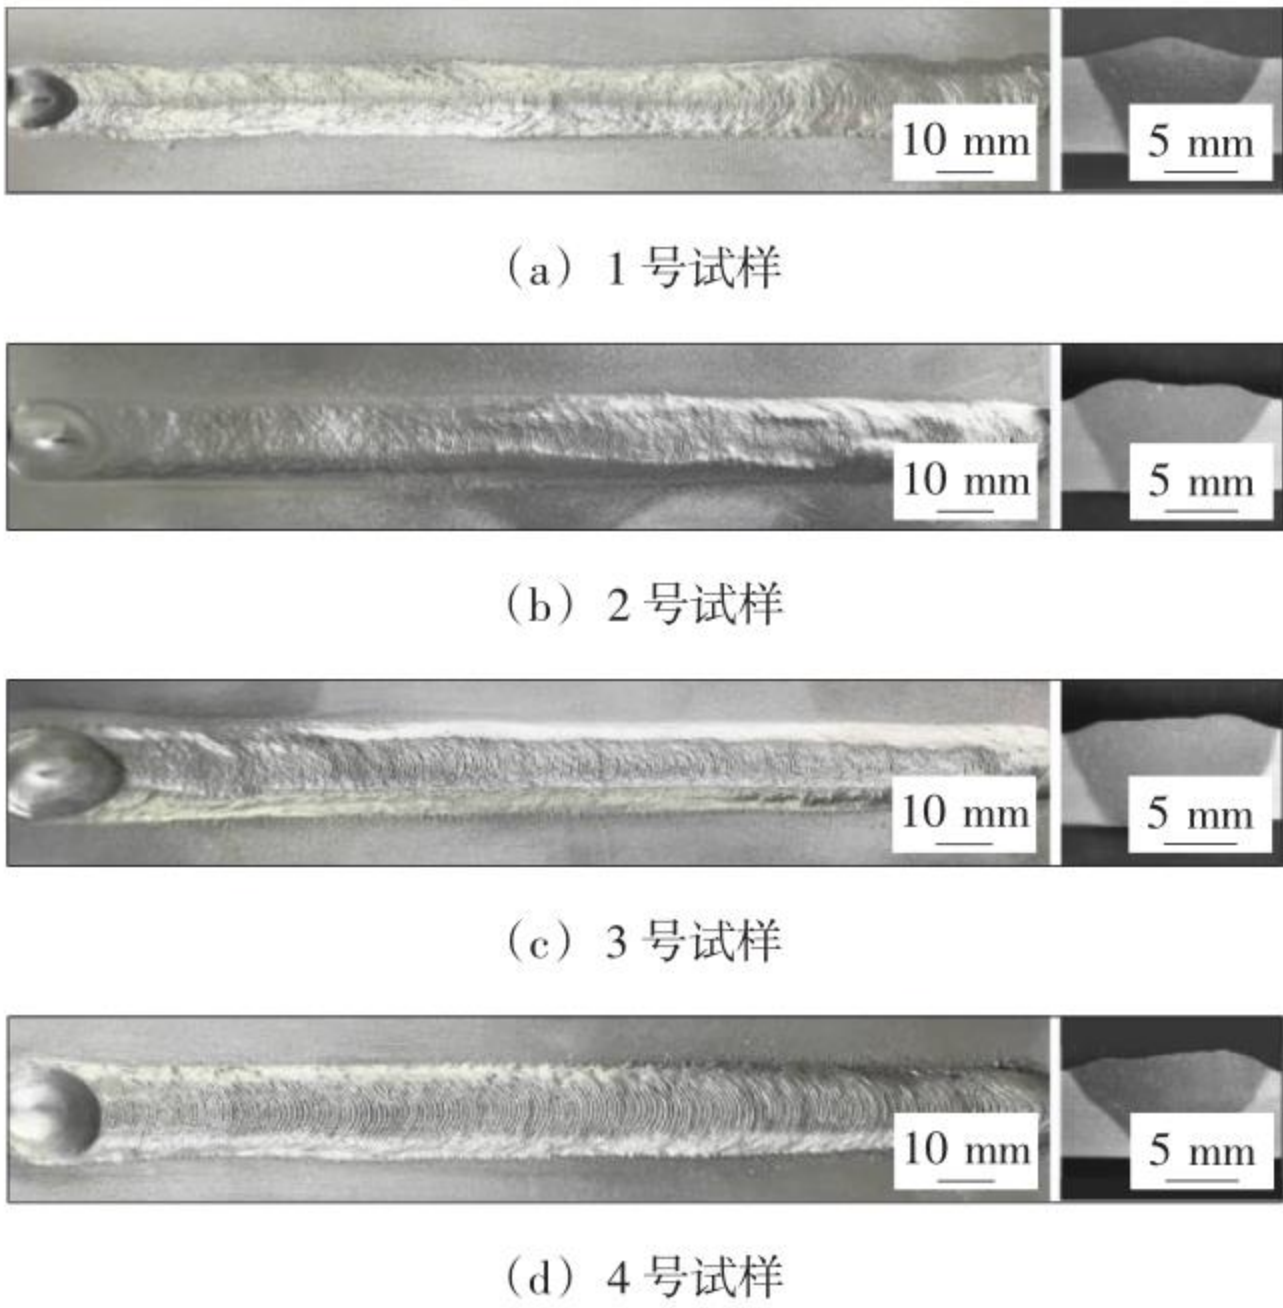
不同焊接工艺参数下的接头焊缝表面和横截面宏观形貌
